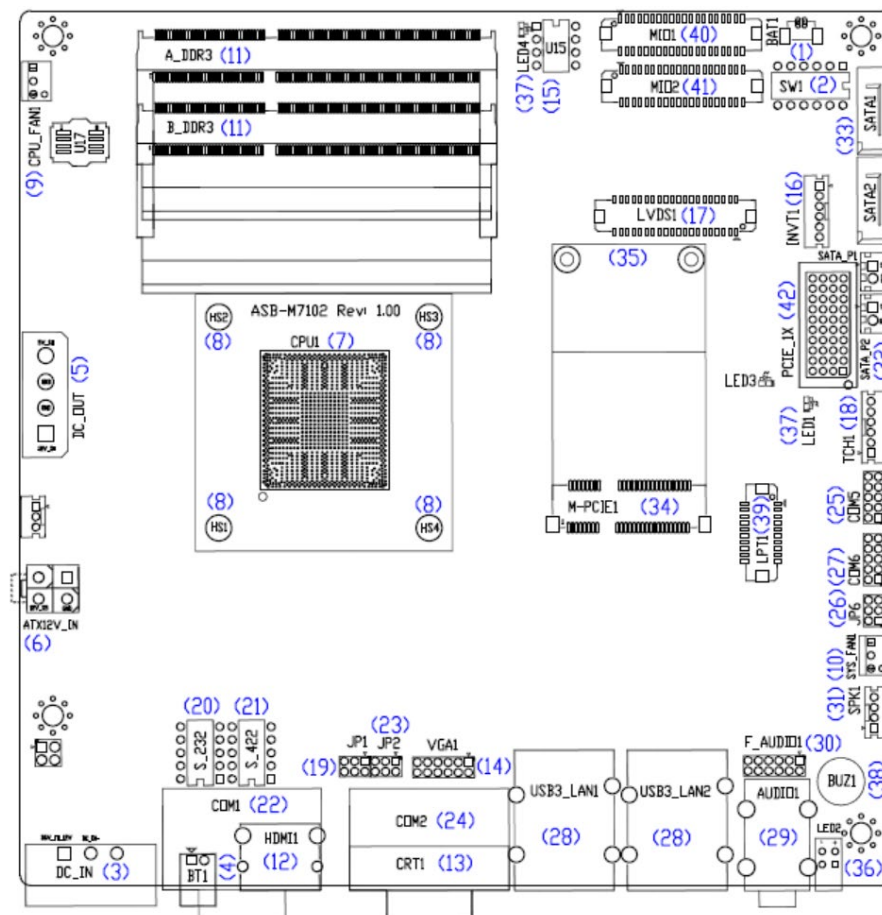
ASB-M7102 - Anschlüsse und Jumper - Draufsicht
